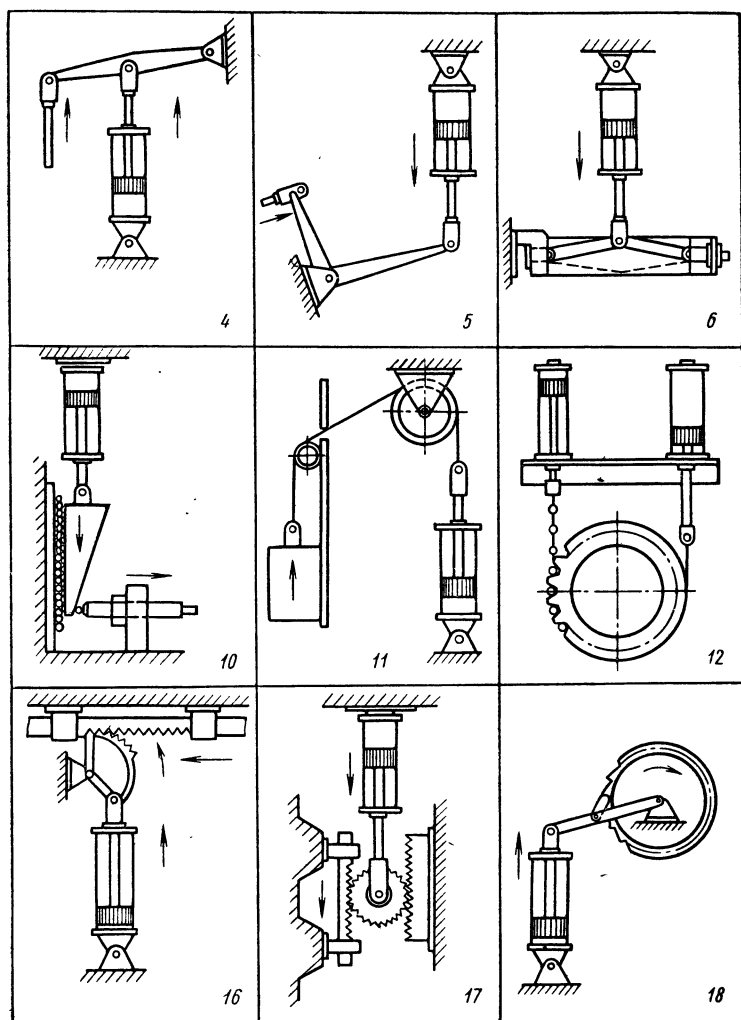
Схемы применения пневмоцилиндров с различными передаточными механизмами:
